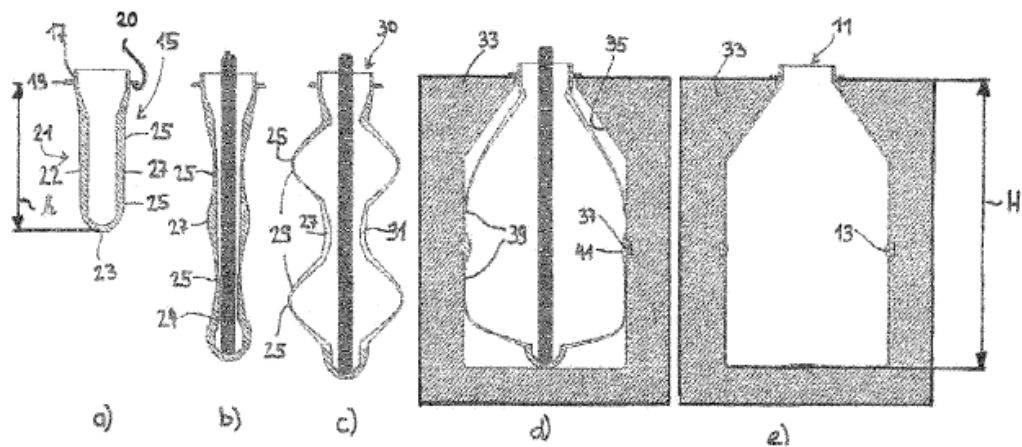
Спосіб виготовлення пластикової пляшкової форми
